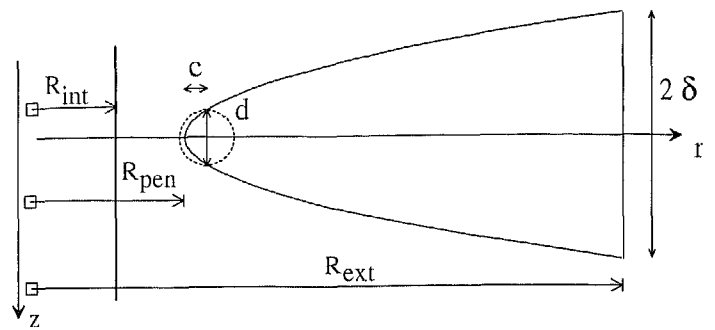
Paramètres du modèle de cordon de soudure.
